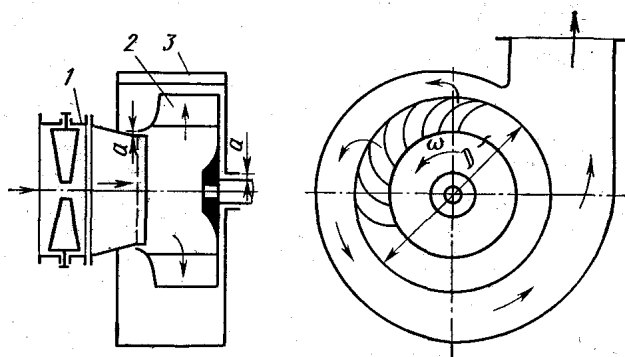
Схема центробежного вентилятора: 1 – подвод; 2 – рабочее колесо; 3 – корпус
